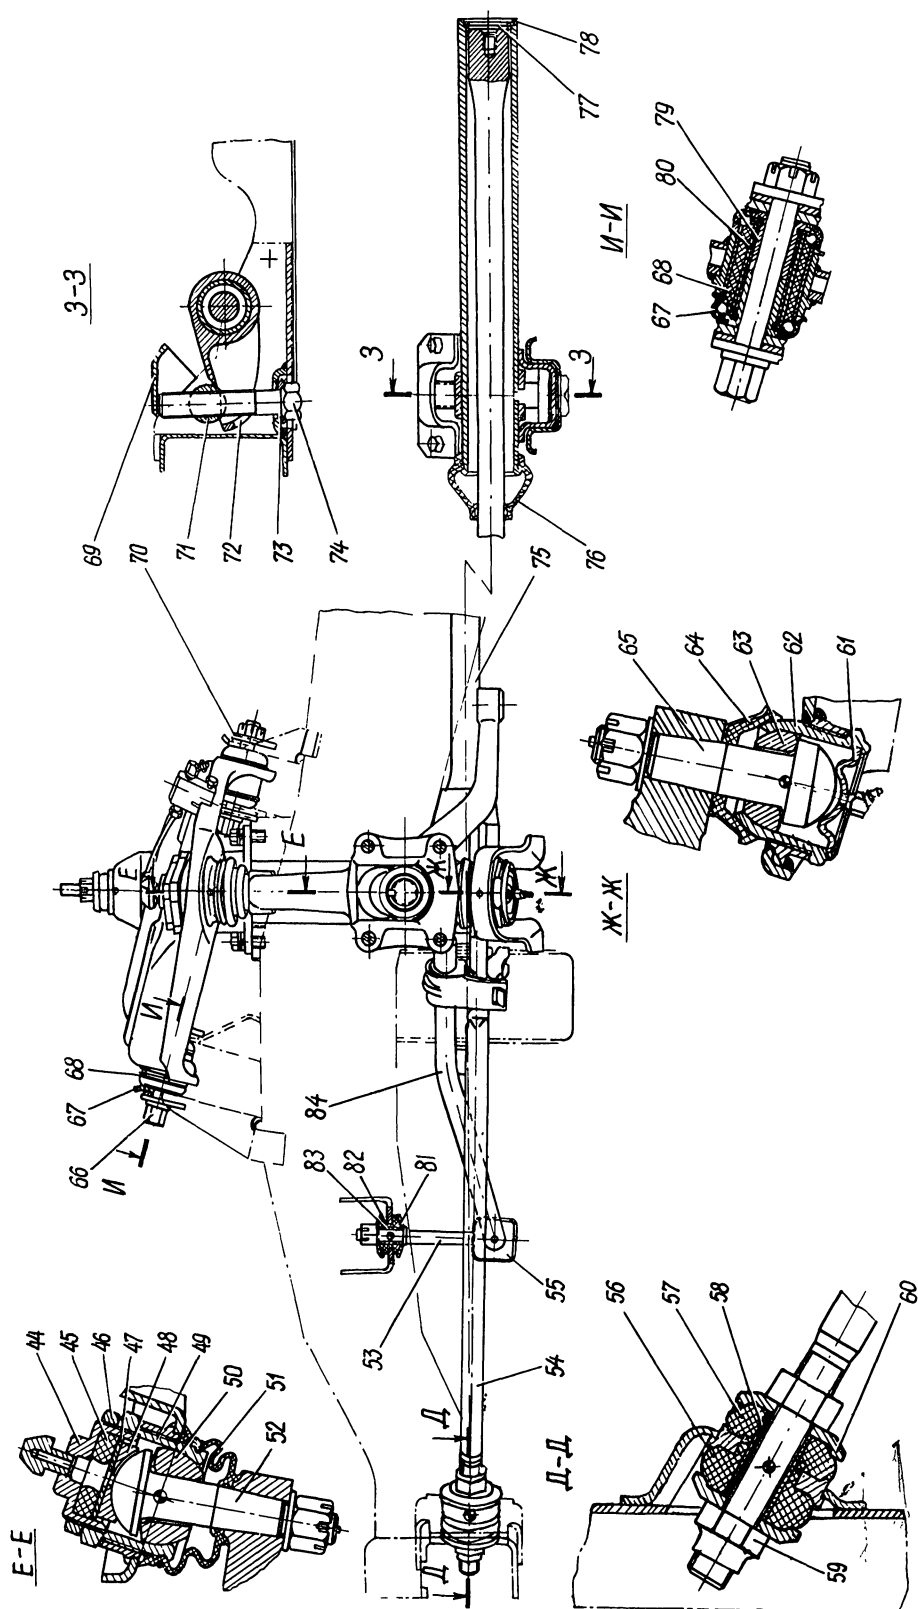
Передняя подвеска с колесами в сборе (вид сбоку)
